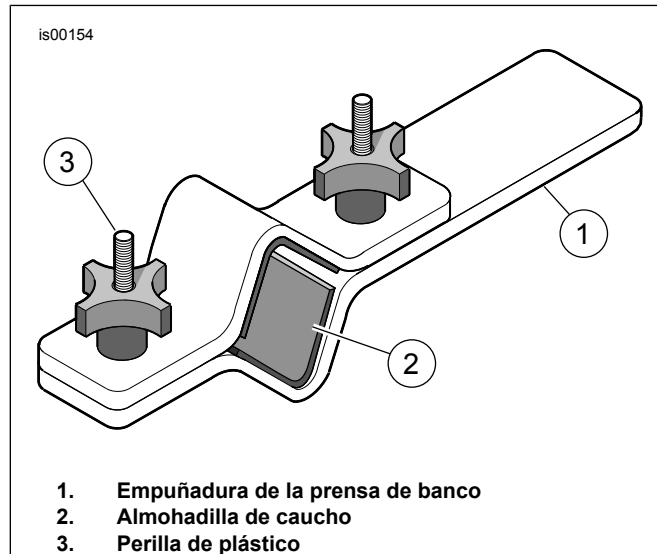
Soporte del tubo de la horquilla (HD-41177)
